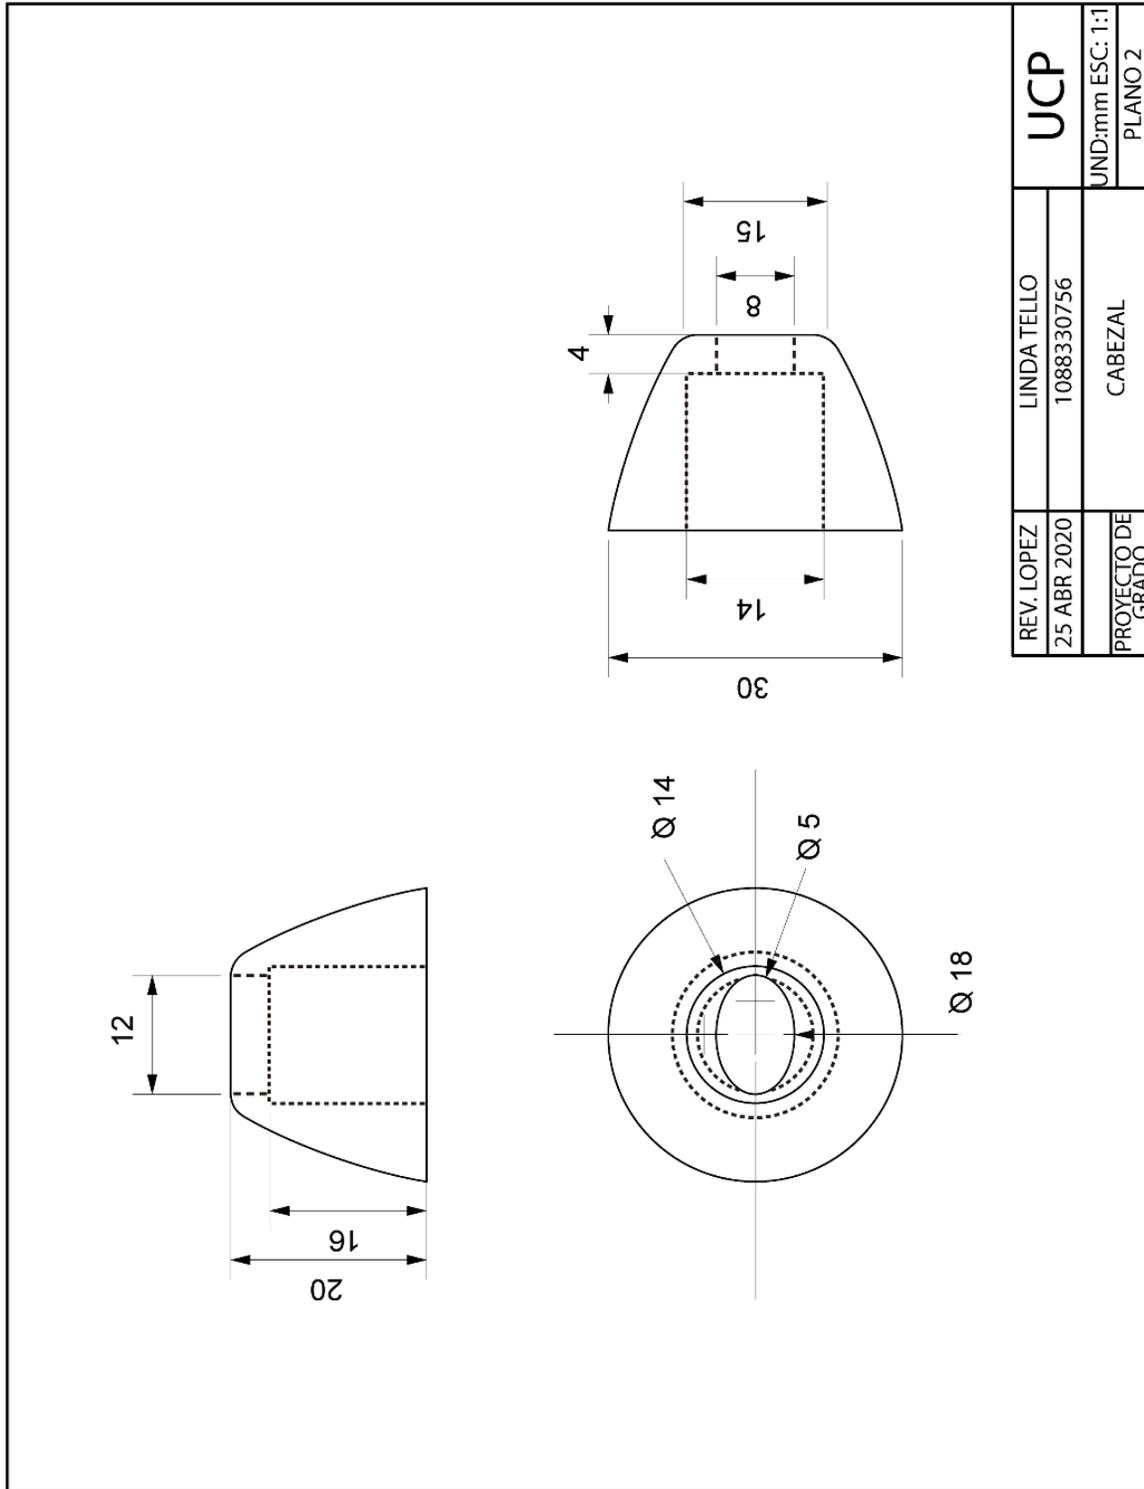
Plano de cabezal. Fuente: Elaboración propia
